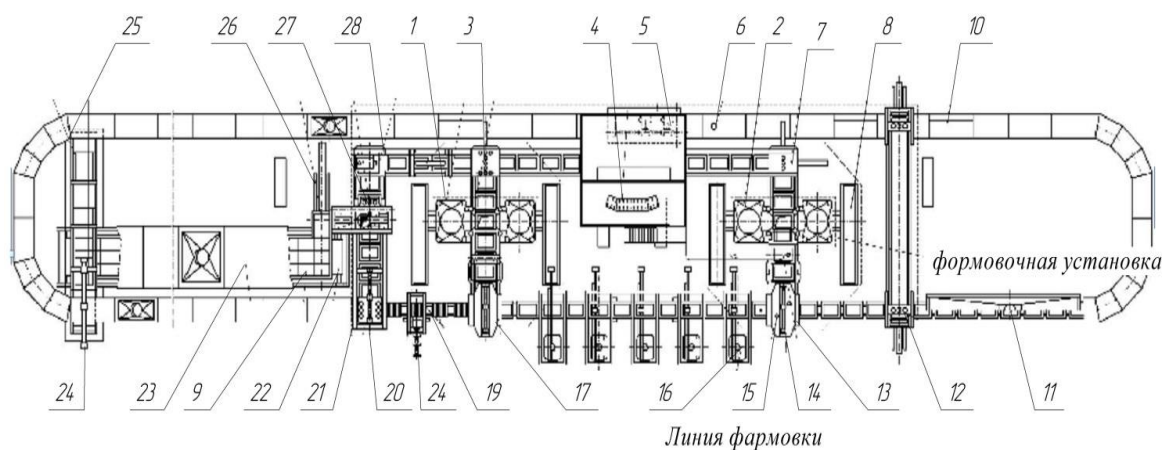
Схема планировки комплексной автоматической линии модели Л450А: 1, 2 - формовочная установка мод. 3019; 3 - распаровщик; 4 - центральный пульт управления; 5 - каретка силовых гидроцилиндров литейного конвейера; 6 - рольганг; 7 - устройство передачи верхних опок к формовочному автомату; 8 - устройство для замены модельных комплектов; 9 - брикеты на конвейере охлаждения; 10 - охлаждающий тоннель; 11 - место заливки; 12 - укладчик грузов; 13 - механизм накалывания вентиляционных каналов; 14 - кантователь верхних полуформ; 15 - сборщик форм; 16 - стержнеукладчик; 17 - устройство передачи нижних полуформ на литейный конвейер; 18 - устройство для срезания излишка смеси; 19 - тележка конвейера; 20 - устройство для очистки тележек; 21 - устройство для передачи залитых форм с литейного конвейера на выбивку; 22 - охлаждающий конвейер; 23 - тоннель интенсивного охлаждения; 24 - толкатель брикетов на выбивку; 25 - выбивная решетка; 26 - толкатель брикетов на конвейер охлаждения; 27 - установка выдавливания брикетов с отливками из опок; 28 - устройство передачи комплекта пустых опок; 29 - литейный пульсирующий конвейер; 30 - кантователь нижних полуформ.
